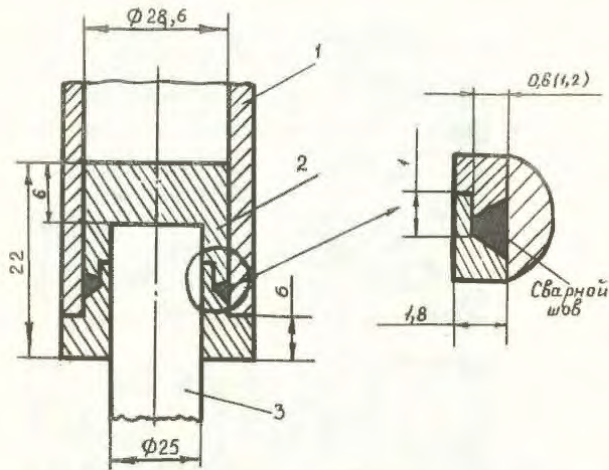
Конфигурация и размеры сварных образцов для динамических и статических испытаний: 1 - опорный стержень; 2 - образец; 3 - стержень-передатчик
